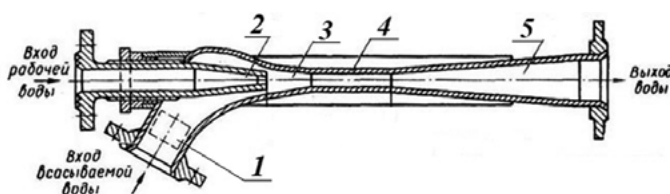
Схема эжектора: 1 — всасывающий патрубок;
